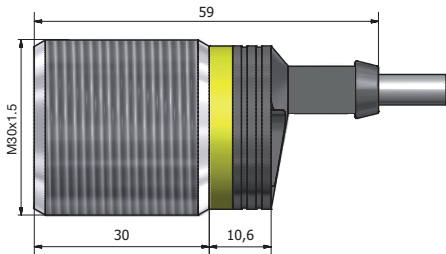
Kurze Ausführung, bündiger Einbau, Kabel
